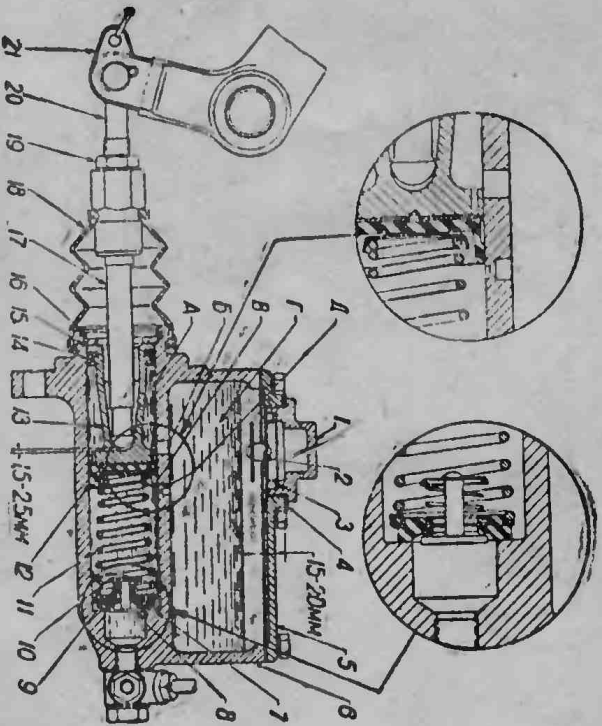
Главный цилиндр гидравлического привода тормозов:
